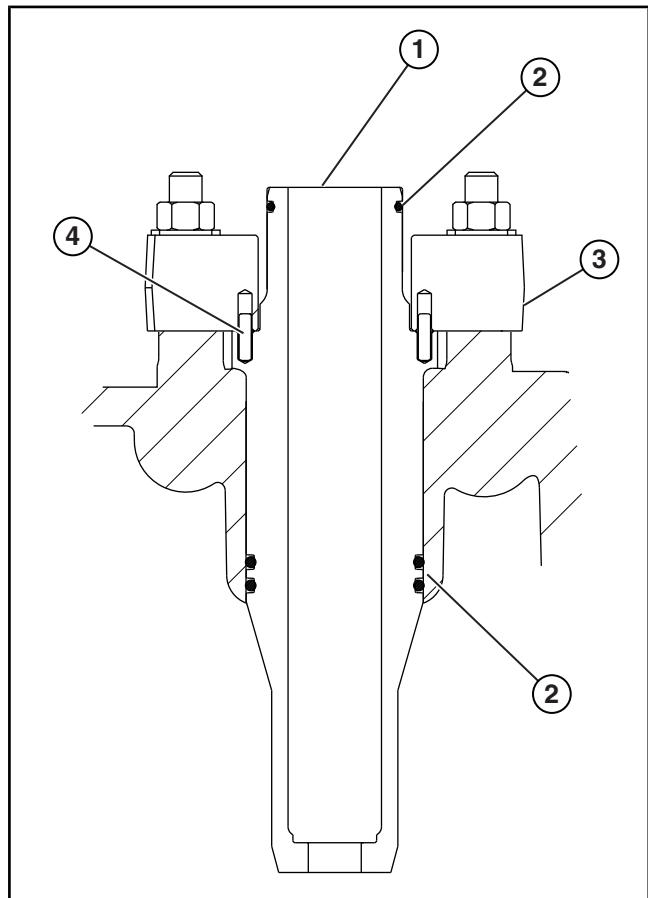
Установка удлинителя втулки свечи зажигания
